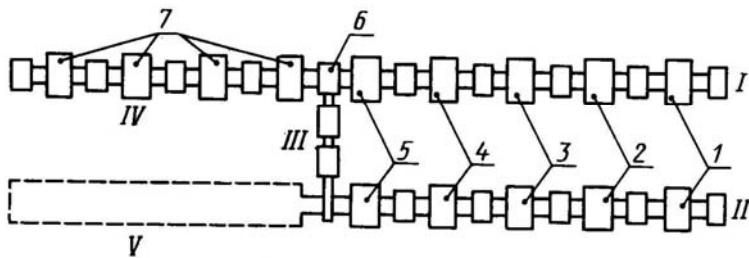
Схема участка сборки и сварки кабин грузового автомобиля ЗИЛ
